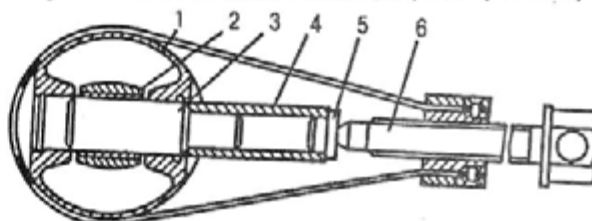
Запрессовка поршневого пальца в поршень и шатун съемником 7823-6102:
